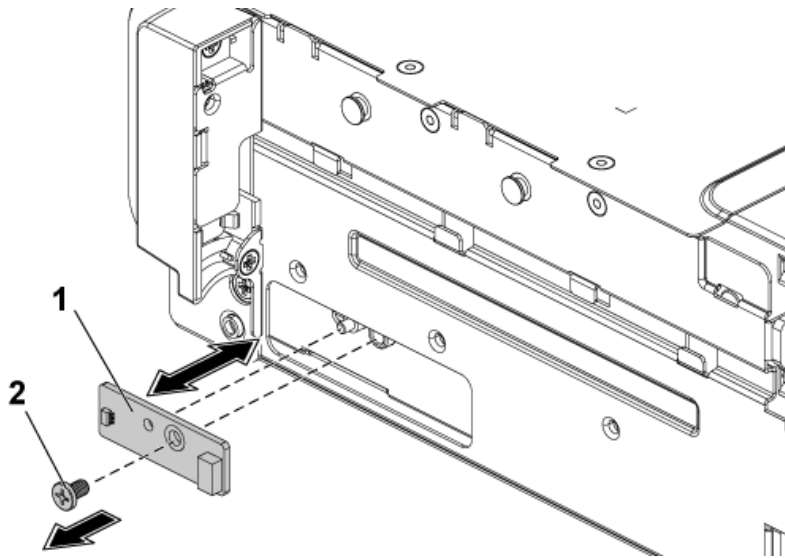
Entfernen und Einsetzen der Sensorplatine
